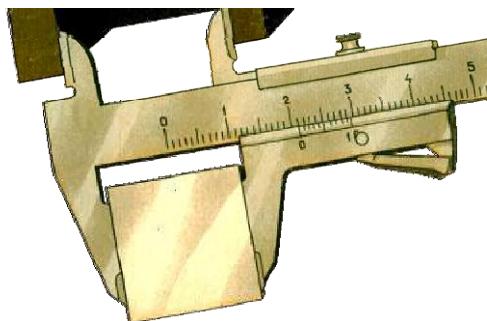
Перевірка паралельності обпилених поверхонь штангенциркулем .
